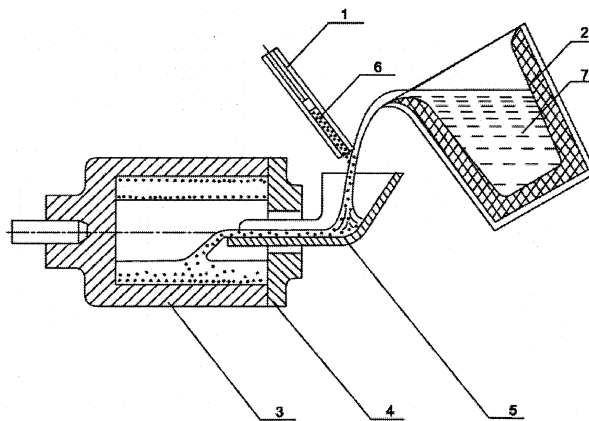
Схема заливки и упрочнения трубной заготовки: 1 – дозатор; 2 – ковш с металлом; 3 – горизонтальная изложница; 4 – крышка изложницы; 5 – сталезаливочный носок; 6 – мелкодисперсные твёрдые тугоплавкие частицы; 7 – расплав
